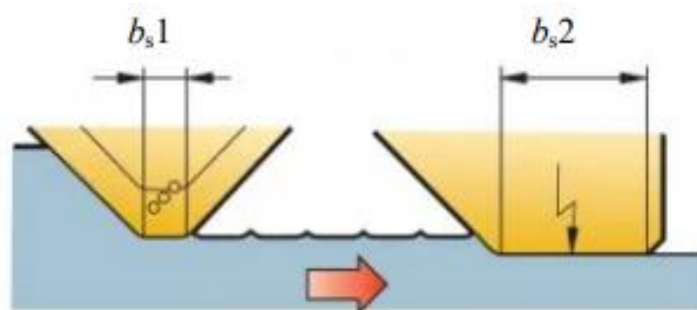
Змінні різальні пластини з геометрією Wiper для зачистки поверхні
